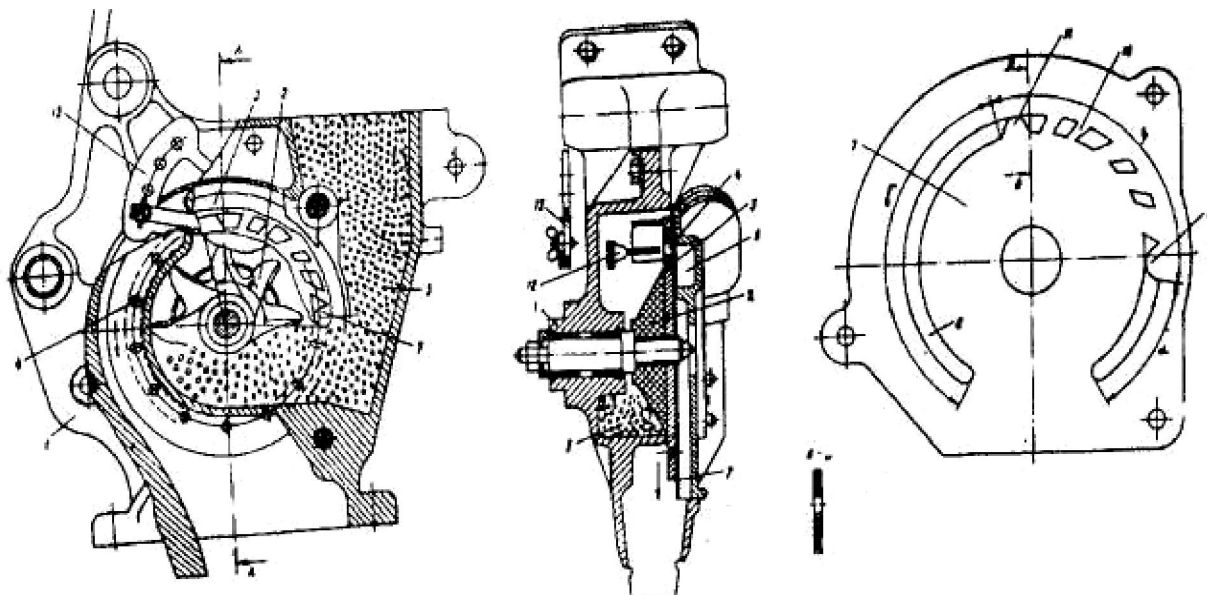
Висівний апарат з комбінованою прокладкою: 1 - корпус; 2 - ворушилка; 3 - висівний диск; 4 - наскрізні отвори диска; 5 - насіннева камера; 6 - вакуумна камера; 7 - капронова комбінована прокладка; 8 - кільцевий виріз; 9, 10, 11 - перемички; 12 - відбивач; 13 - регулятор відбивача
